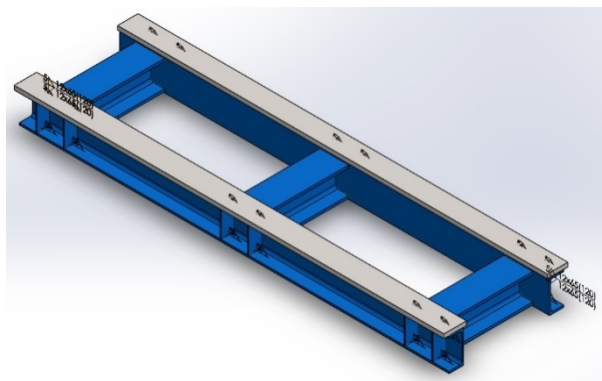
Bancada de apoyo del panel soldada
